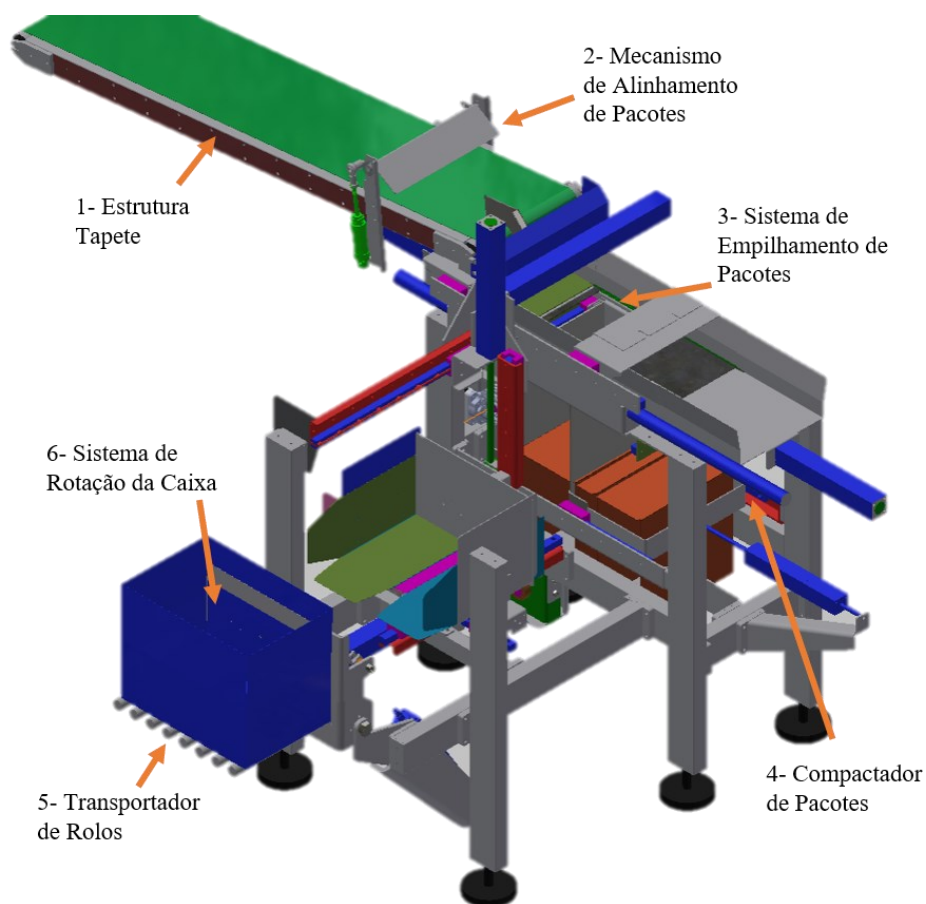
Sistema de enchimento vista 1 CAD 3D
